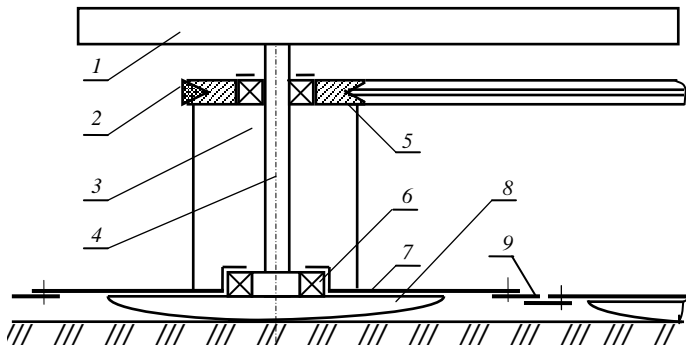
Схема ротора двухроторной косилки с механическим приводом:
